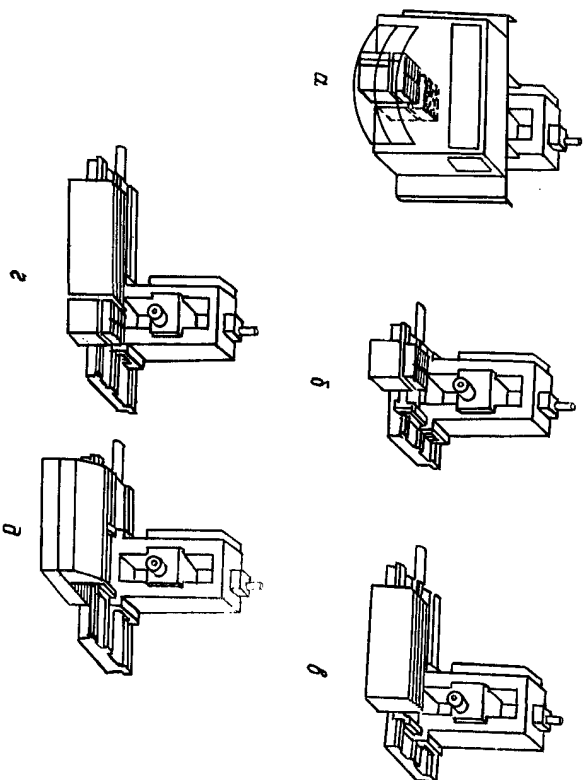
Примеры типовых конструкций обрабатывающего центра типа С-ГБSSW-800 со сварными модулями и различной компоновкой рабочих столов:
